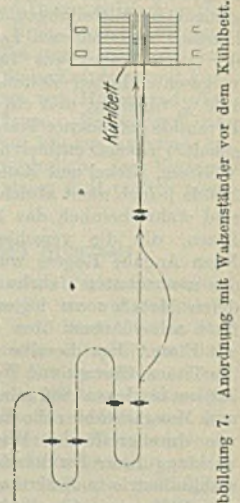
Anordnung mit Walzenständen vor dem Kühlbett.
